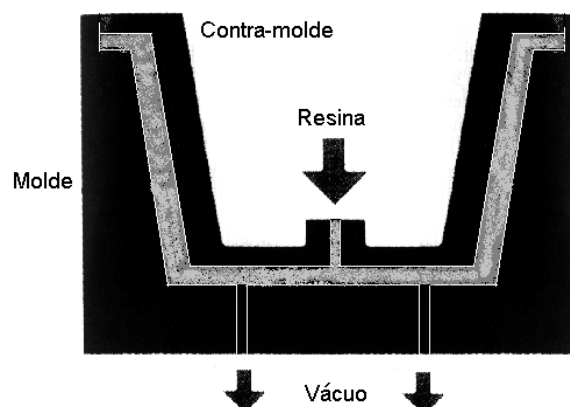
Moldagem por injeção assistida por vácuo (VARI)[7].
